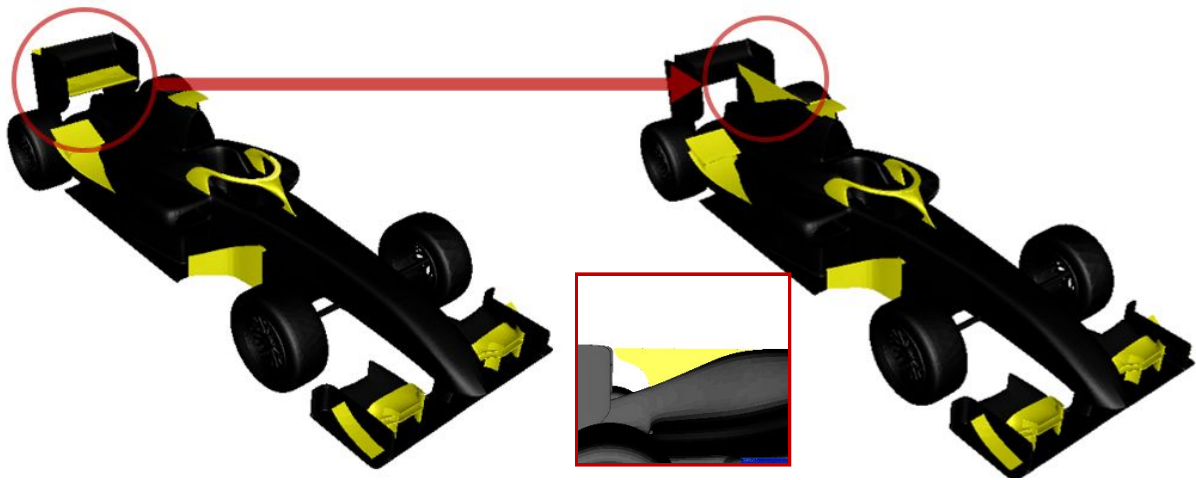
Remplacement de l'aileron arrière par un aileron de requin
